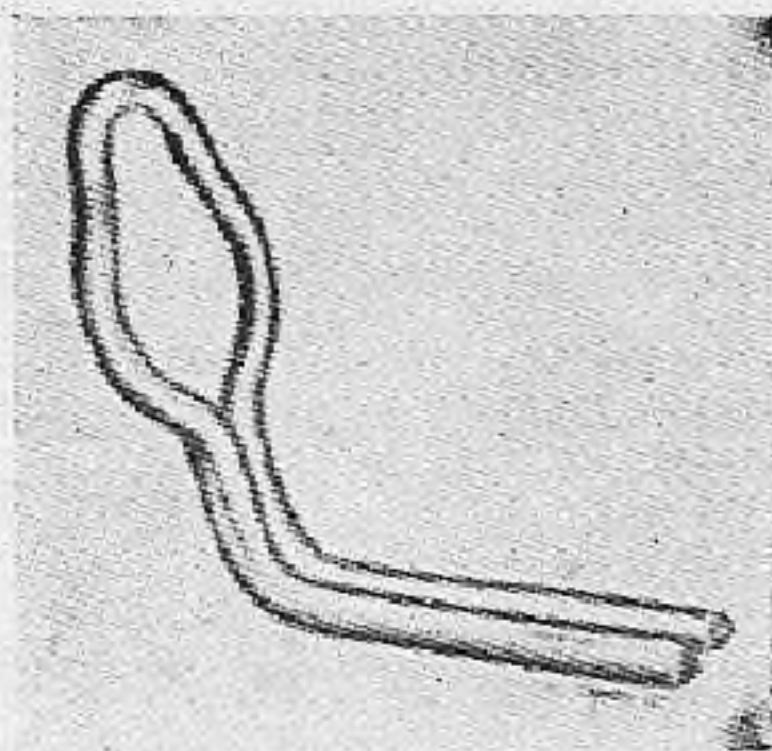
Herramienta para desmontar y montar el ornamento metálico frontal (relleno moldura) del marco del parabrisas.
